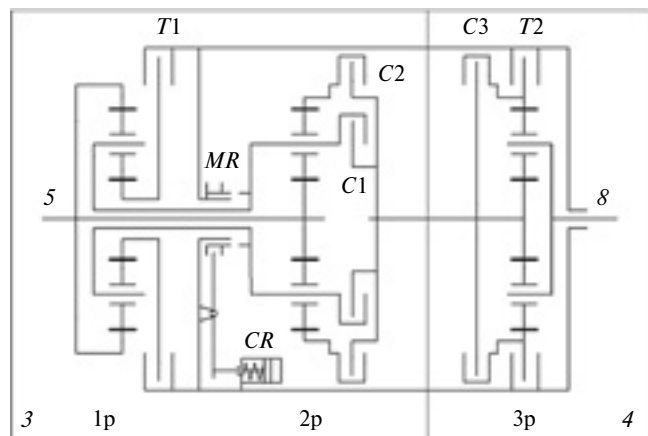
Схема планетарной коробки передач с включением ступени заднего хода зубчатой муфтой (обозначения поз. 3, 4, 5 и 8 те же, что на рис. 1)
